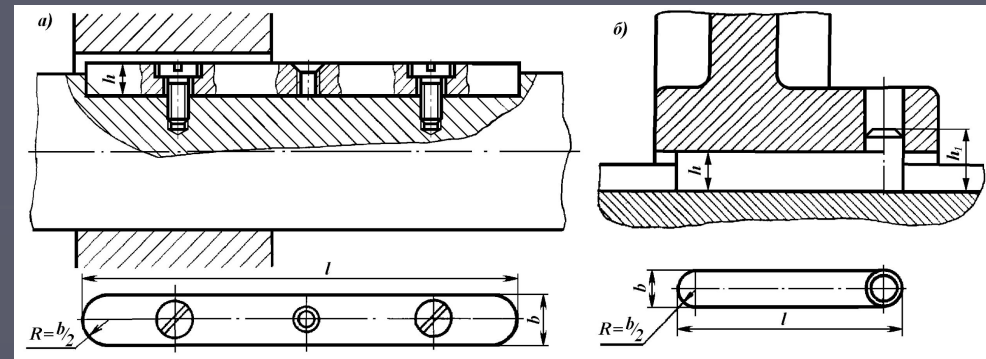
Неподвижное соединение призматической шпонкой.
